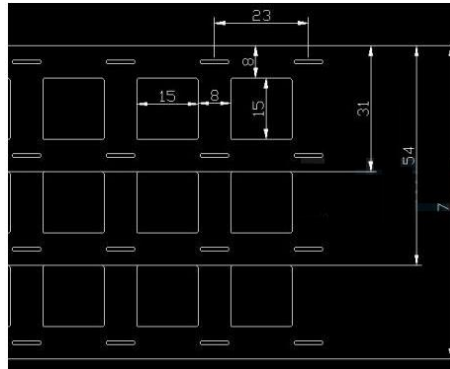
Dimensionado pletina del conexionado entre celdas. Fuente: shoptronica.com
